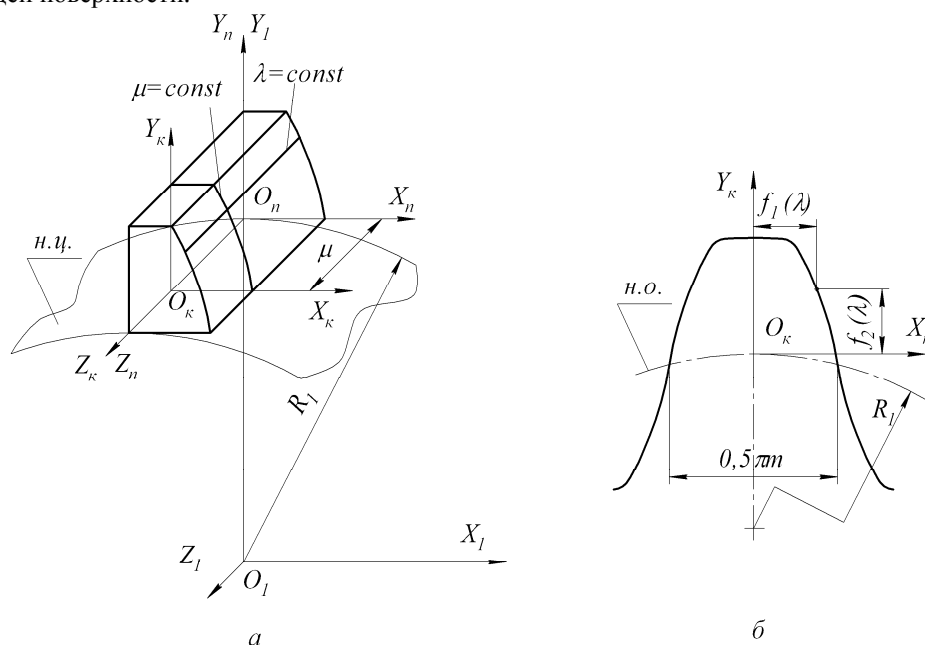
Обобщенная геометрия инструментального колеса:
